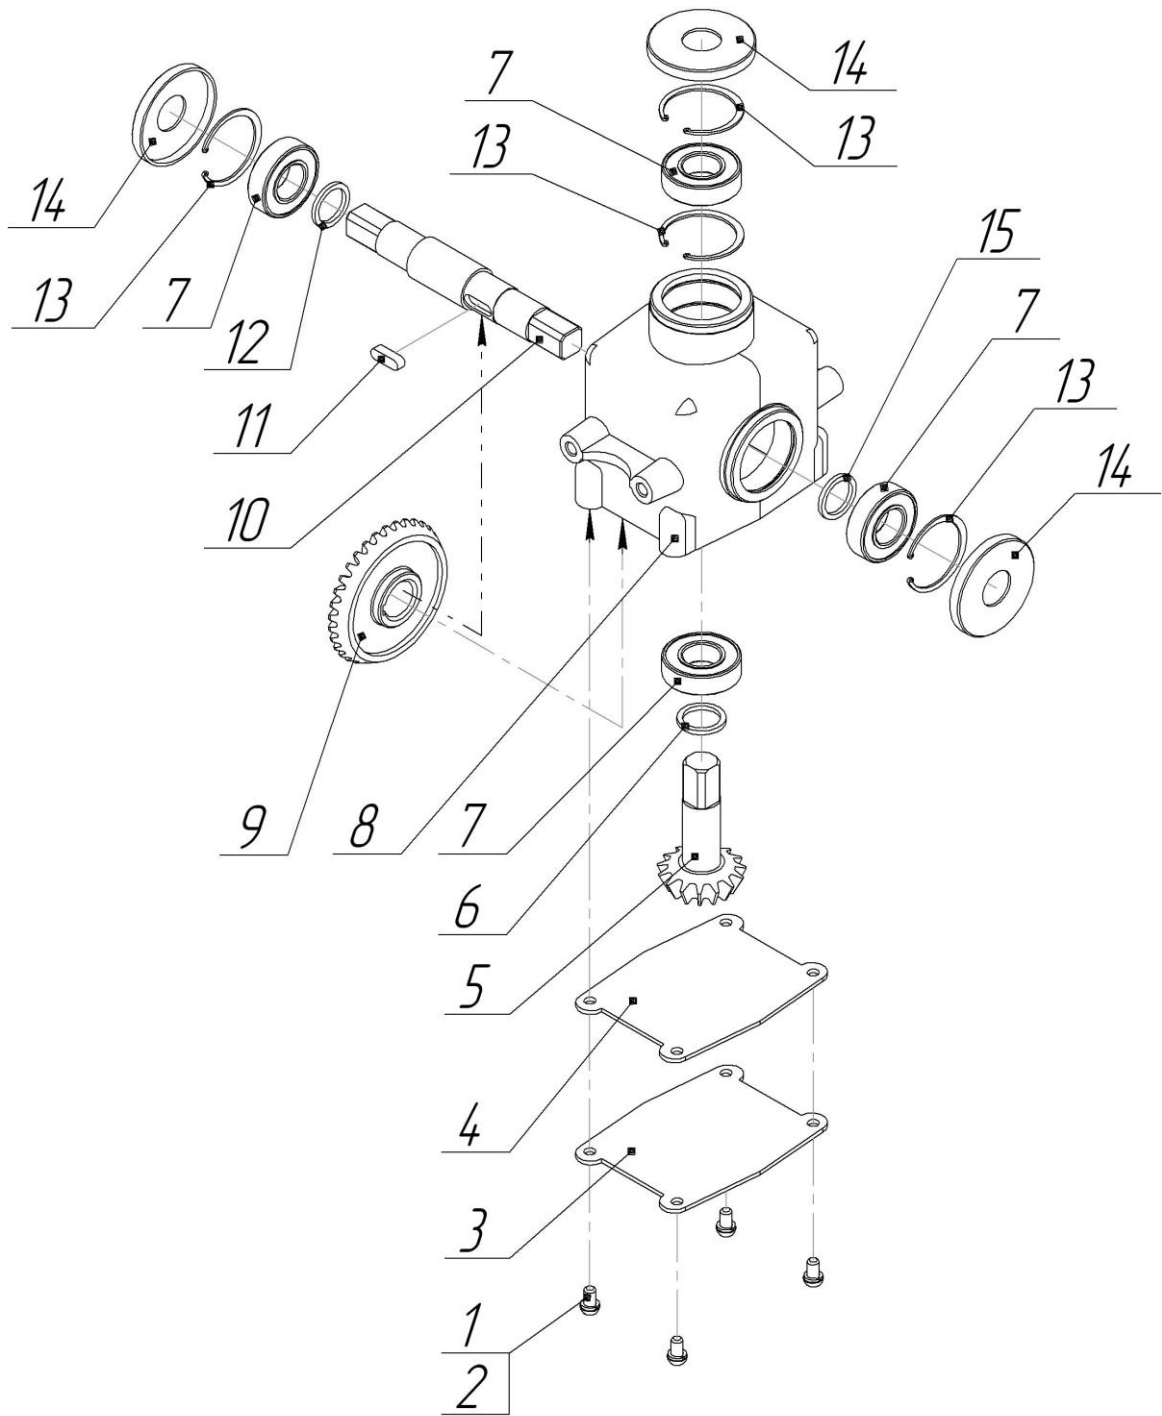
Редуктор шнека загрузочного ИЯПБ 11.73.00.000.
